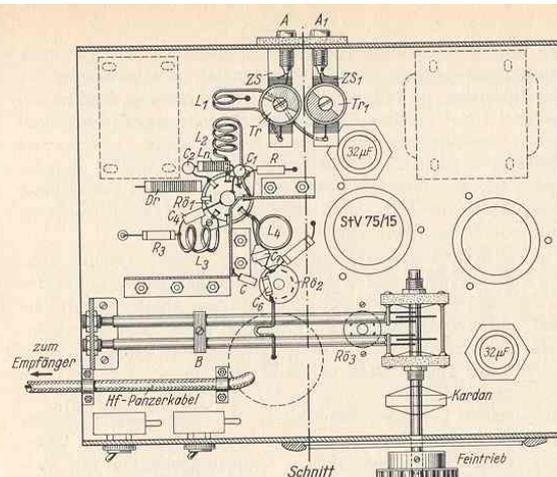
Konstruktionszeichnung für den Kaskoden-Konverter, Ansicht von unten. Maßstab 1 : 3
